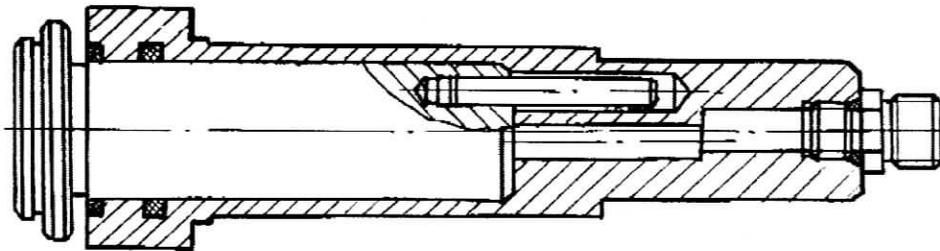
Гидроцилиндр Н.065.15.020А-01 (вариатора мотовила)
